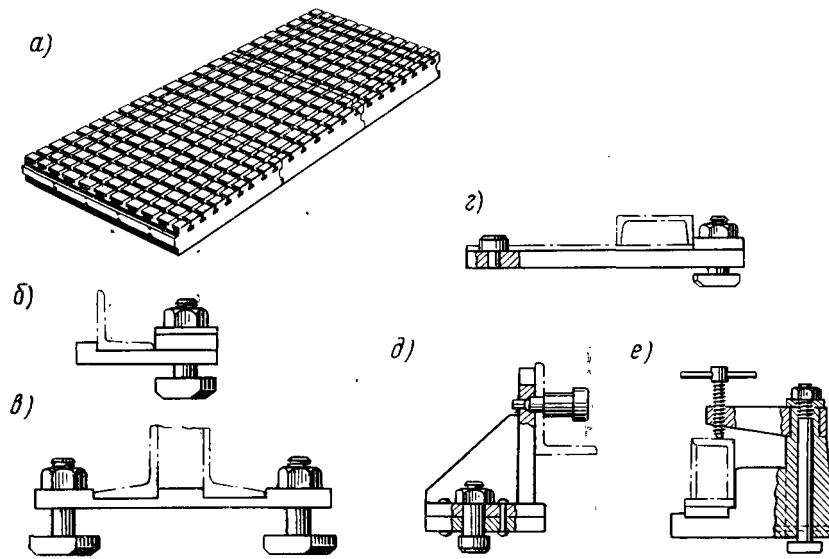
Конструктивные элементы сборных приспособлений:
